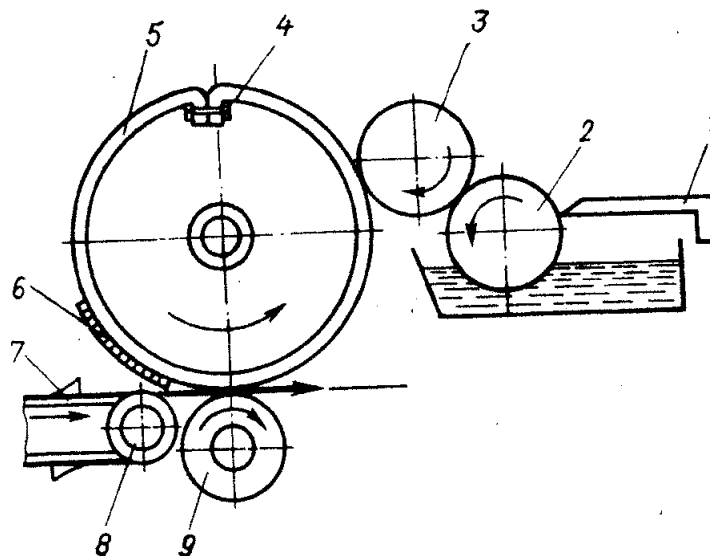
Принцип работы клеющего устройства: 1 – клеевой шабер; 2 – клеевой черпальный валик; 3 – растирающий валик; 4 – затяжной узел резинового полотна; 5 – резиновое полотно клеющего цилиндра; 6 – клише для нанесения клея; 7 – захват конвейерной цепи; 8 – звездочка цепи; 9 – прижимной валик
